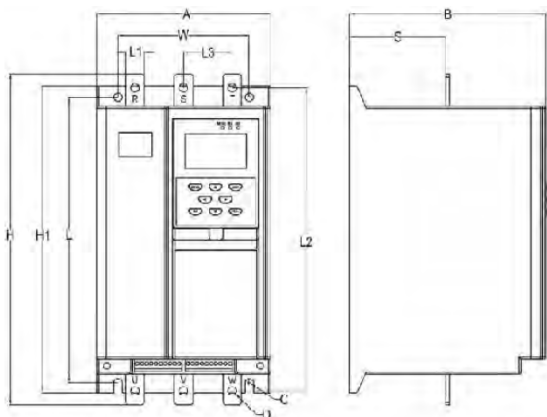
Габаритные и установочные размеры корпуса и медных шин для кода RR1.
